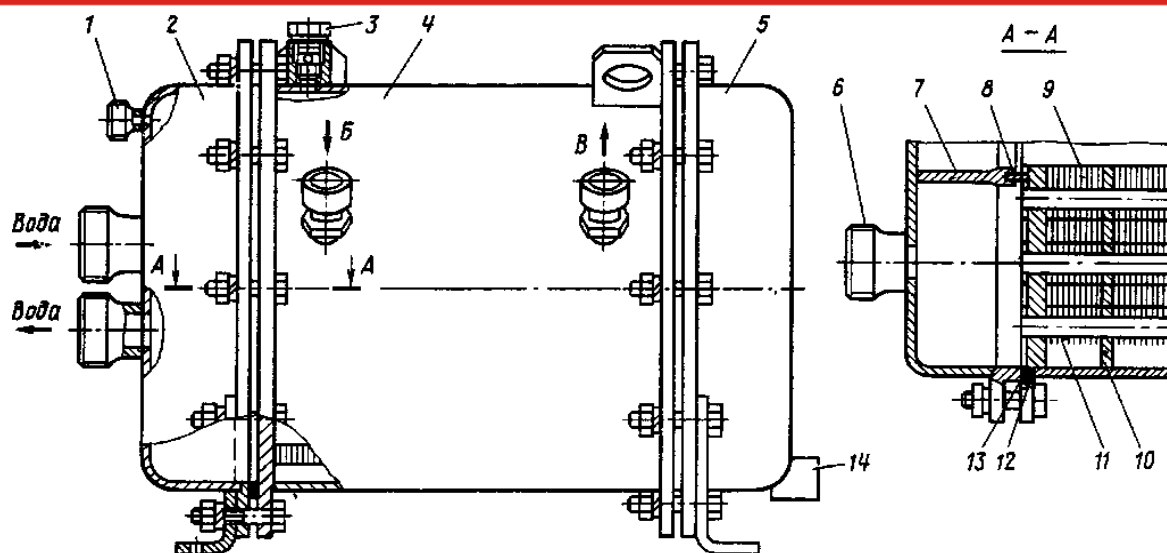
Подогреватель топлива: 1, 6-штуцера; 2, 5-крышки; 3-болт полый; 4-корпус подогревателя топлива; 7, 10-перегородки; 8, 13-прокладки; 9-пластина охлаждающая; 11-трубка; 12-трубная доска; 14-бойка.
